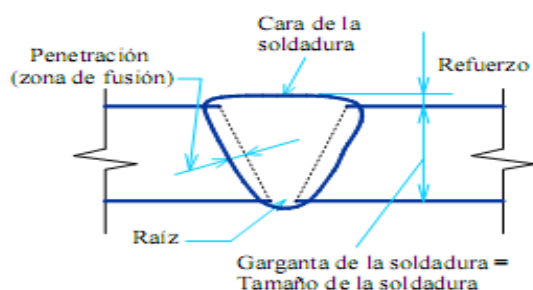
Preparación de la unión para la soldadura.
